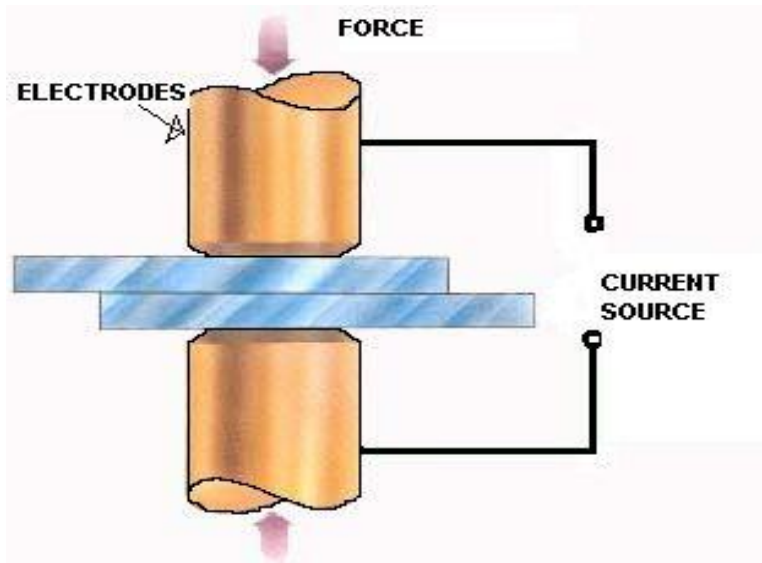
Diferentes tipos de soldaduras por resistencia.
